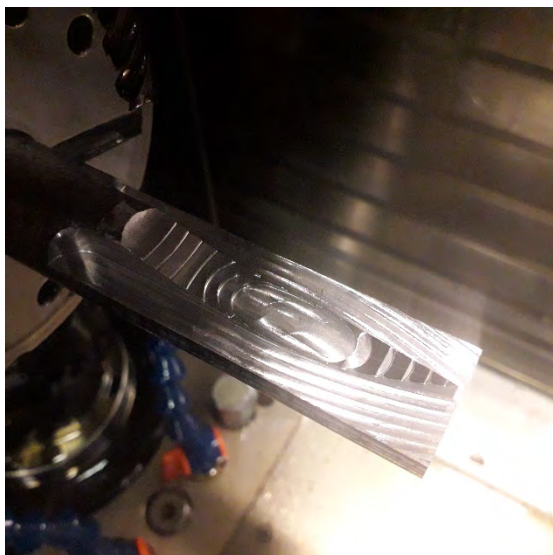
Черновое фрезерование вогнутой наружной поверхности детали на $\frac{1}{2}$ длины заготовки
